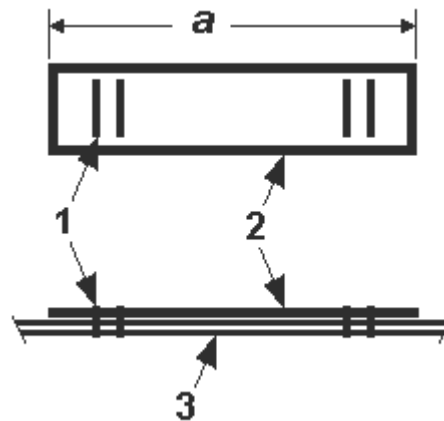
Patrón de corte de la funda (fundas exterior e interior)
